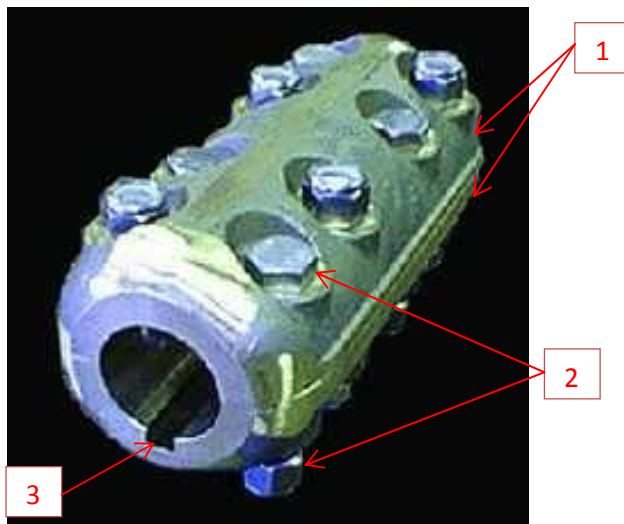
detalle acoplamiento mecánico entre ejes (<http://www.workboatshow.com> y modificada por José M<sup>a</sup> Ros)
